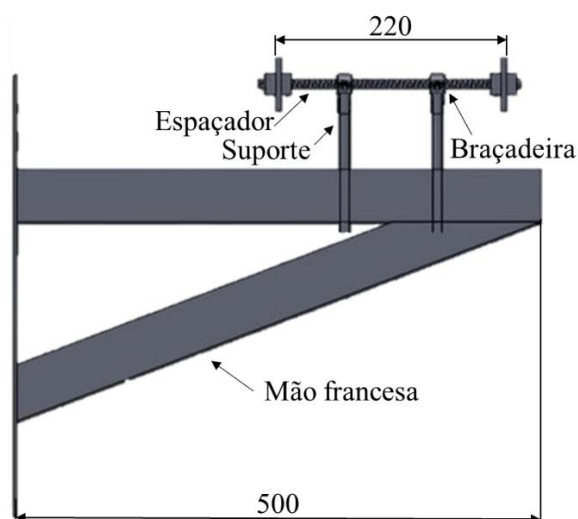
Projeto final da estrutura de fixação. Fonte: Arquivos LabTerm.
